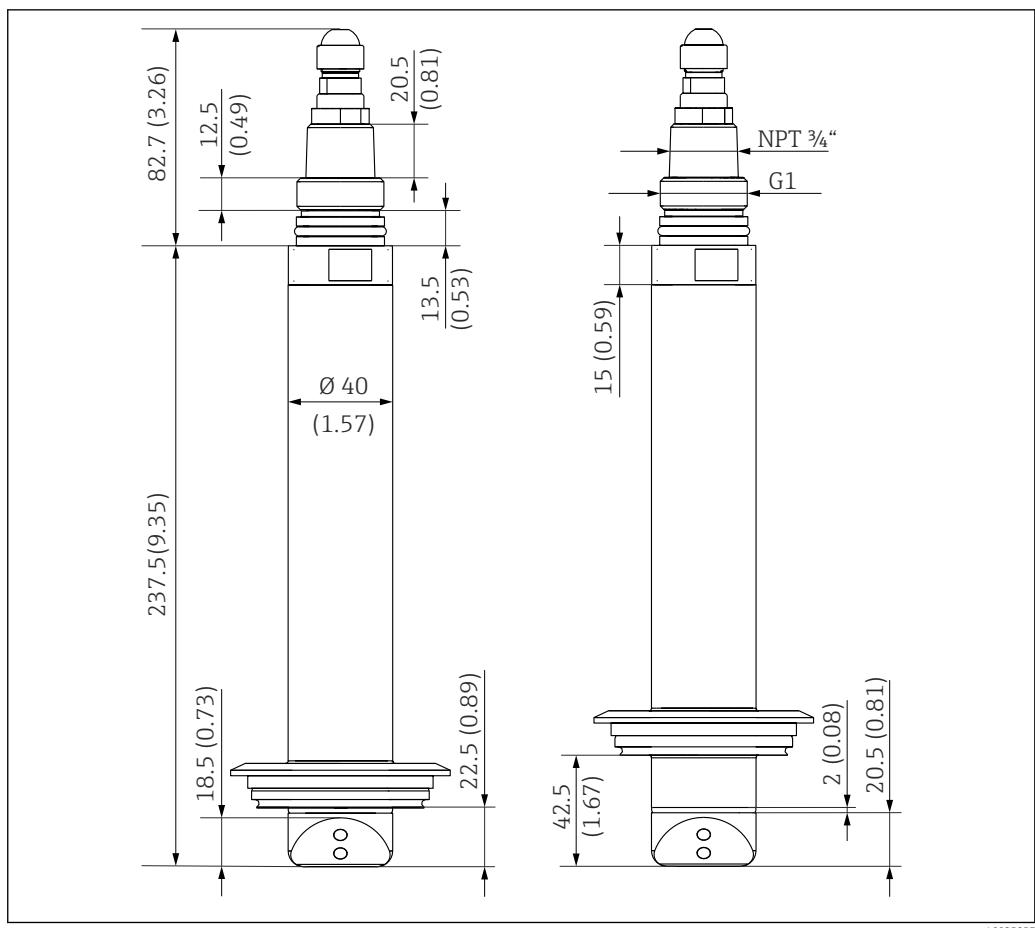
Dimensions du capteur plastique. Dimensions : mm (in)
